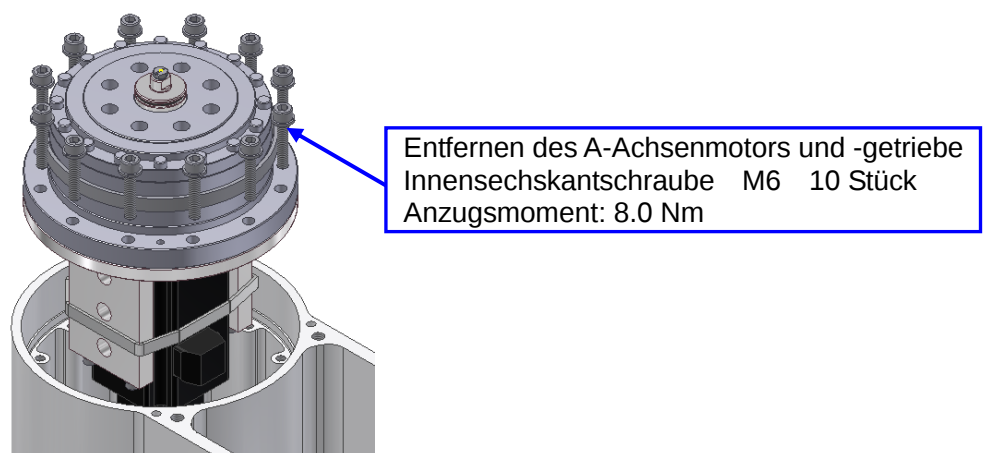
Entfernen des A-Achsenmotors und -getriebe
